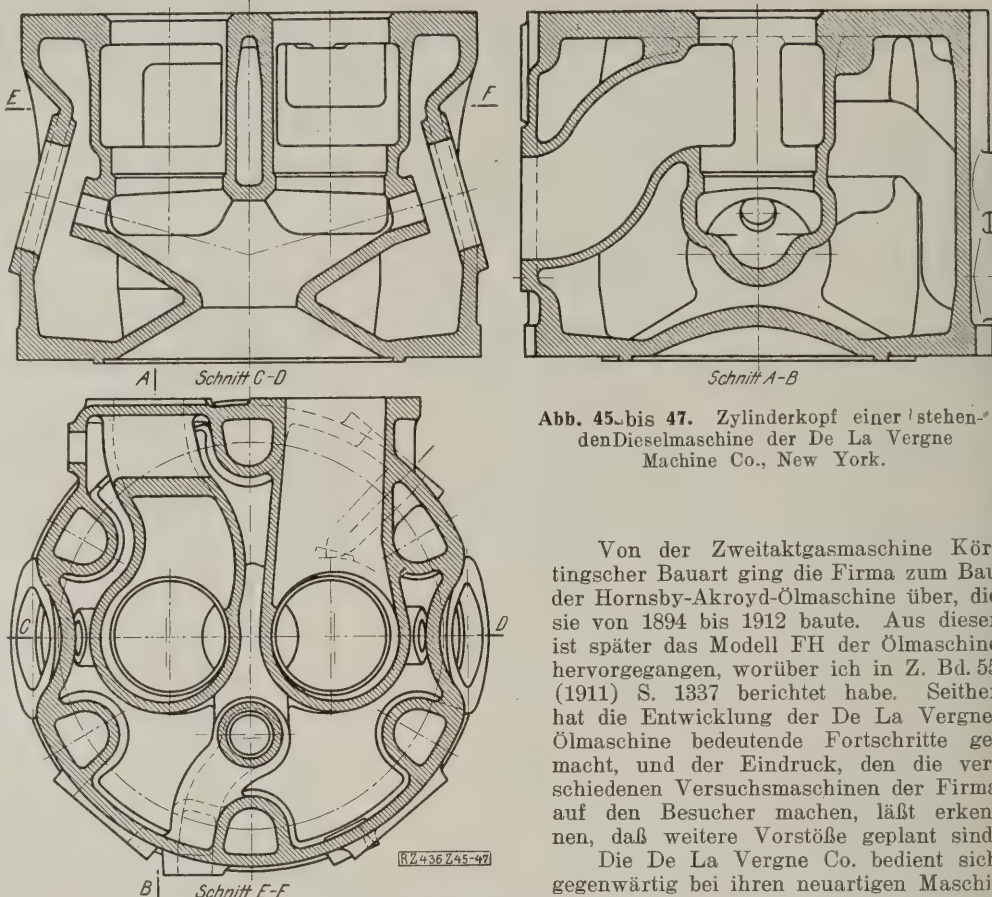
bis 47. Zylinderkopf einer stehenden Dieselmachine der De La Vergne Machine Co., New York.
